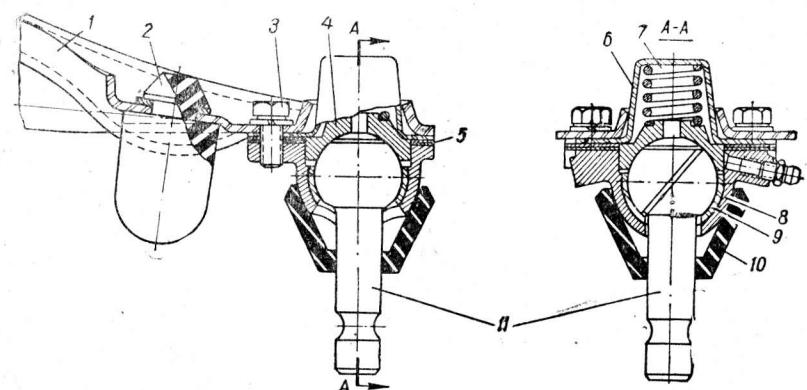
Верхний шаровой шарнир стойки подвески передних колес:
